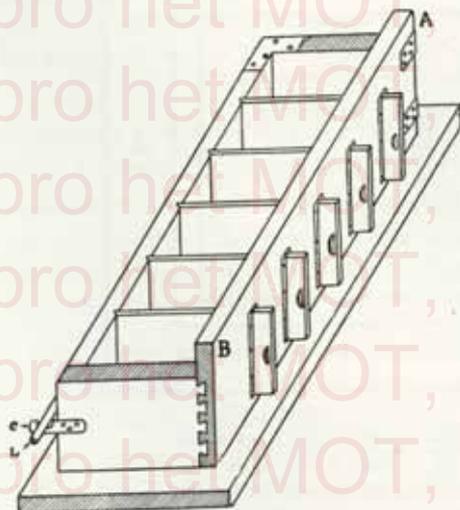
Moule pour la fabrication simultanée de plusieurs blocs.
